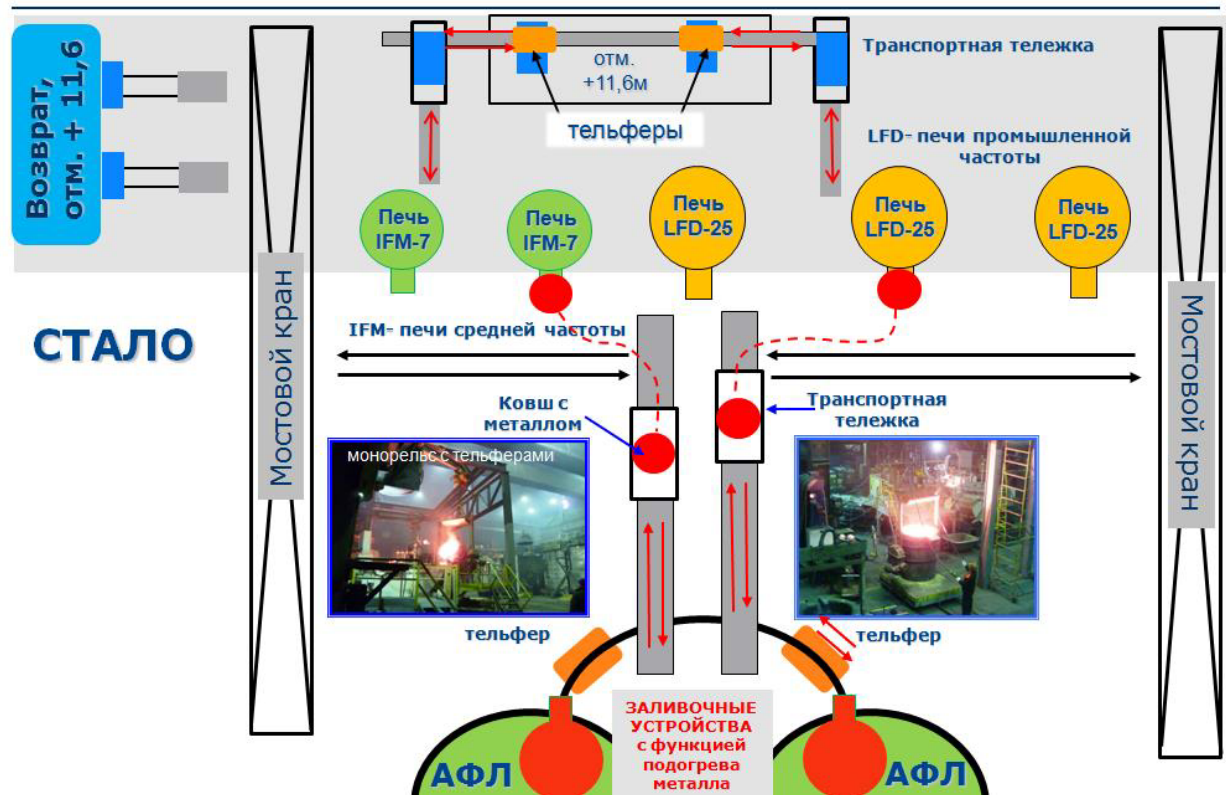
Стало. Плавильный участок - поток транспортировки жидкого металла.
